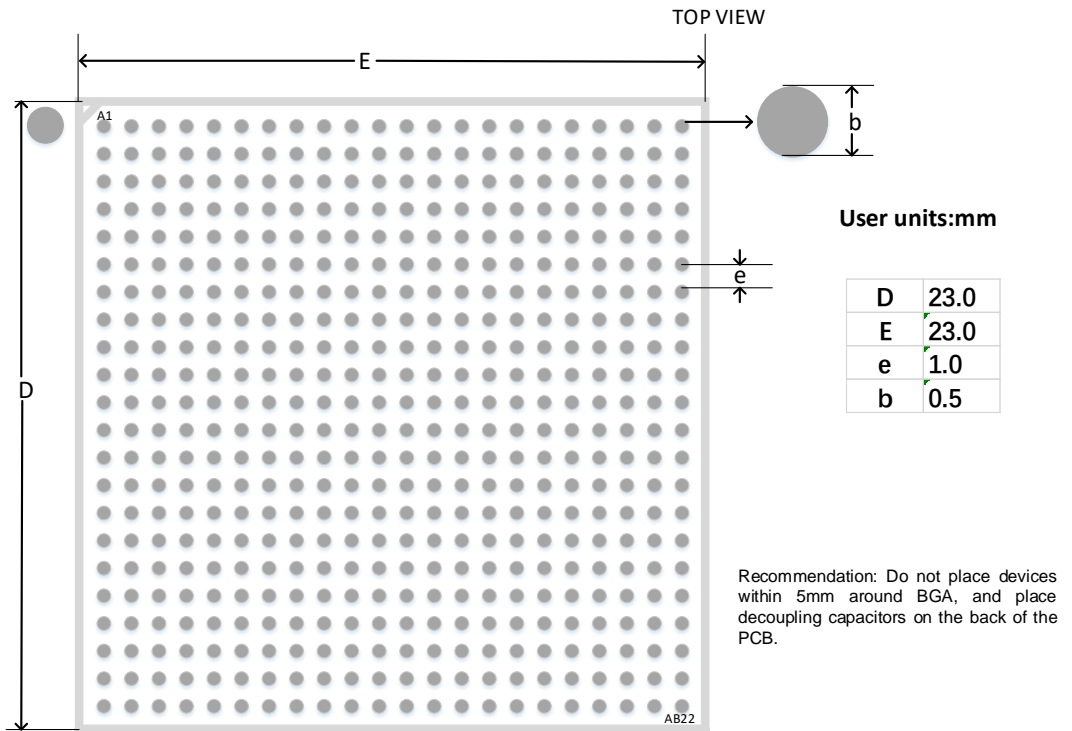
推荐 PCB Layout PG484A (GW5AT-138)
